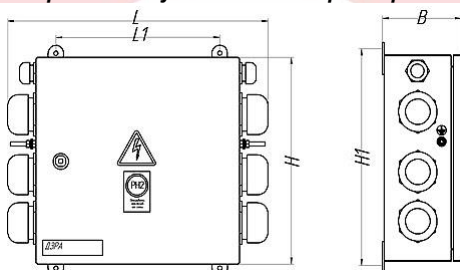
Общий вид, габаритные и установочные размеры КСР-ПП
